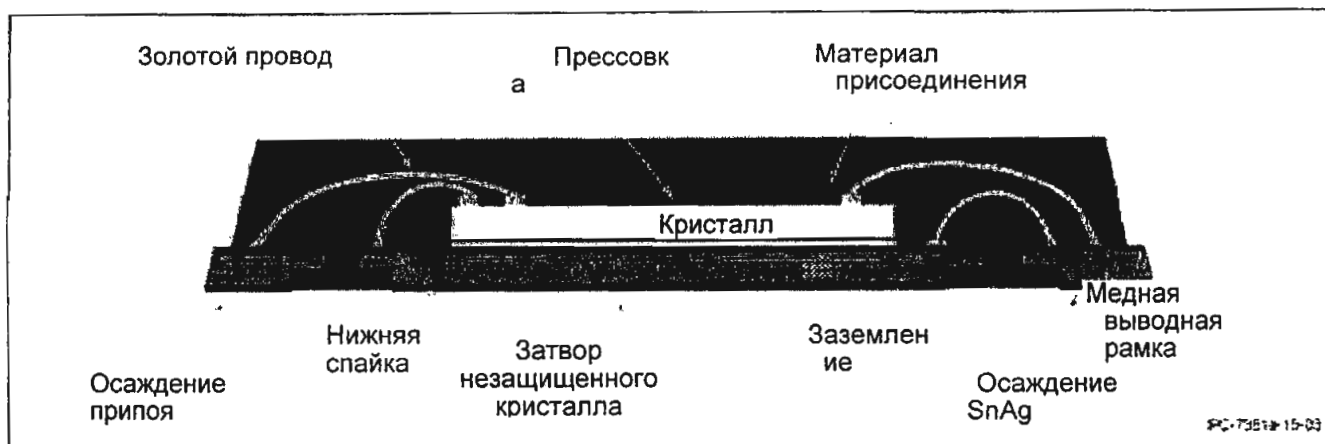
Конструкция плоского безвыводного корпуса с четырехсторонним расположением контактов (QFN) (вид поперечного сечения)
